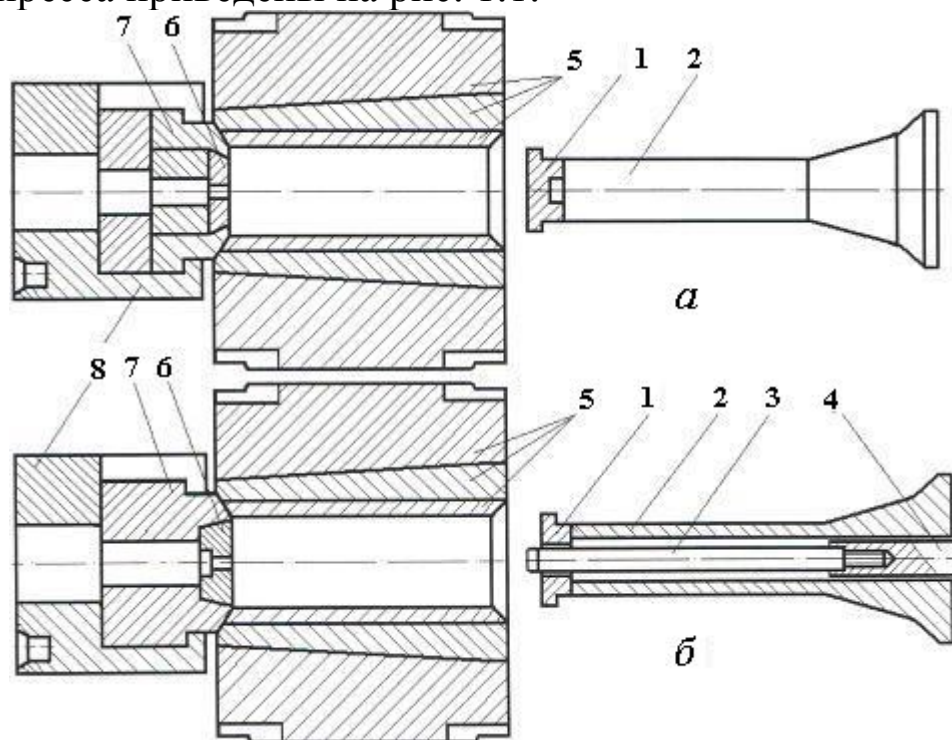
Схема сборки основного инструмента горизонтального гидравлического прутковопрофильного - *а* и трубопрофильного - *б* прессов: 1 – пресс-шайба; 2 – пресс-штемпель; 3 – игла; 4 – иглодержатель; 5 – контейнер (сборный); 6 – матрица; 7 – матрицедержатель; 8 – подвижная (мундштучная) головка или инструментальная доска
